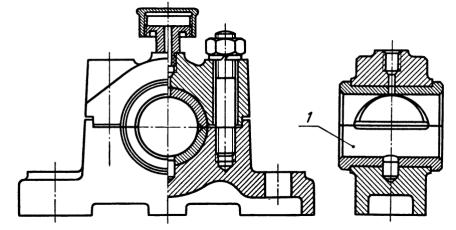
Подшипник с разъемным корпусом и вкладышем
